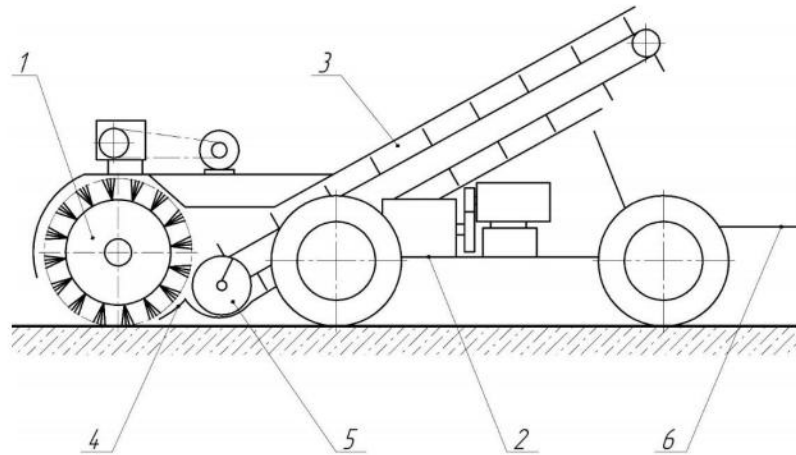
Конструктивно - технологічна схема мобільного щіткового очищувача стійл від гною: 1 - щітковий барабан; 2 - самохідний візок; 3-скребковий транспортер; 4 - прийомний совок; 5 - шнек; 6 - бункер
